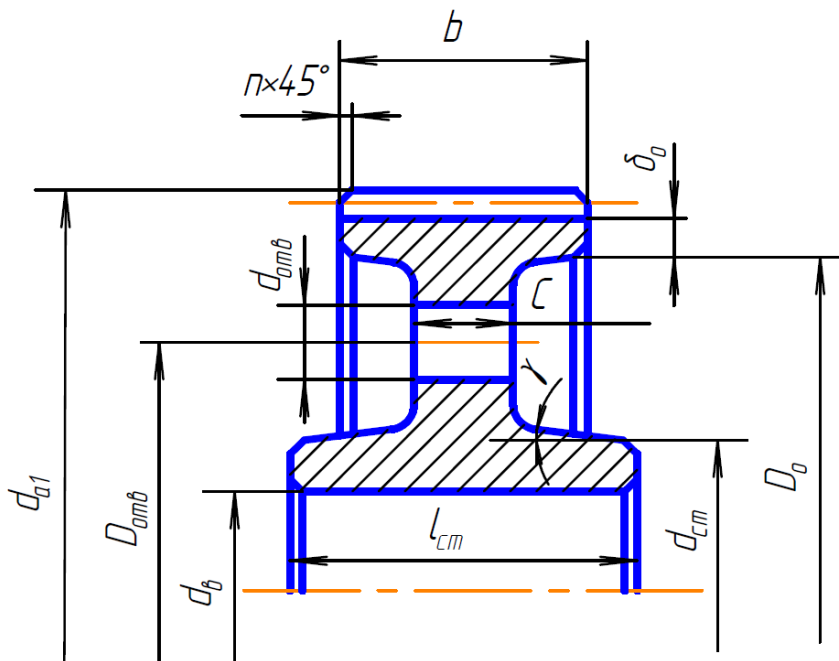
Конструкція циліндричного зубчастого колеса
